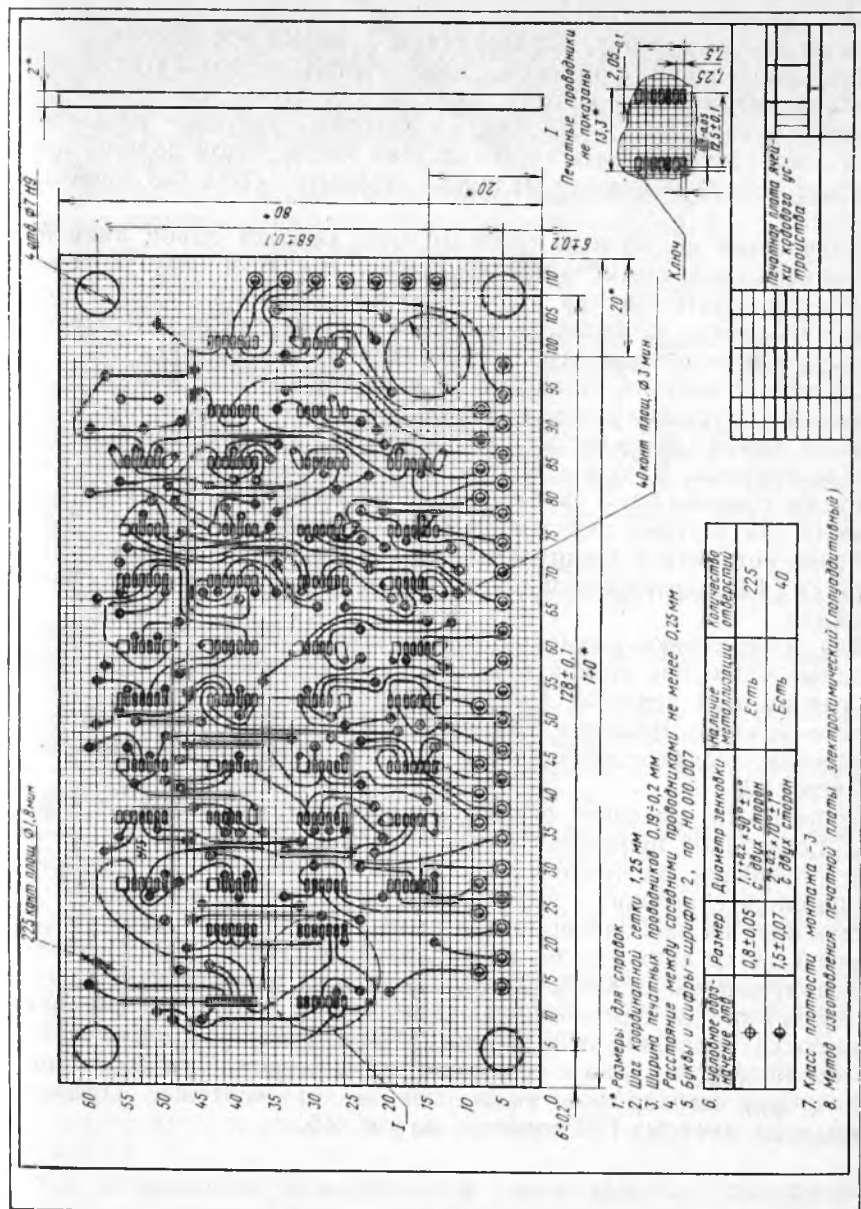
Чертеж печатной платы кодировочного устройства
